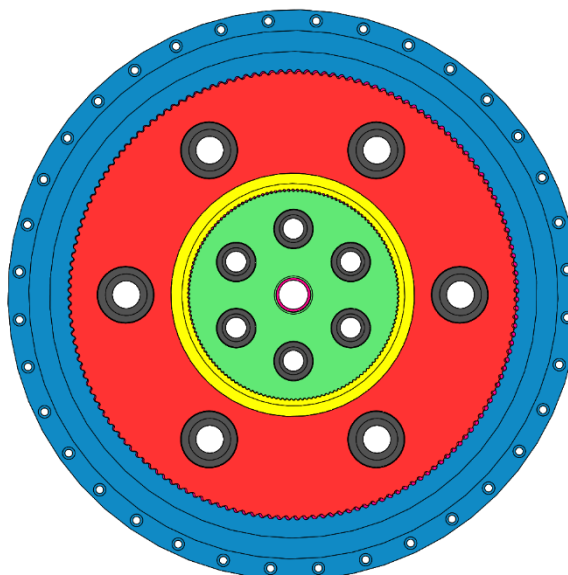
Оптимизированный двухступенчатый редуктор с осевым расположением
